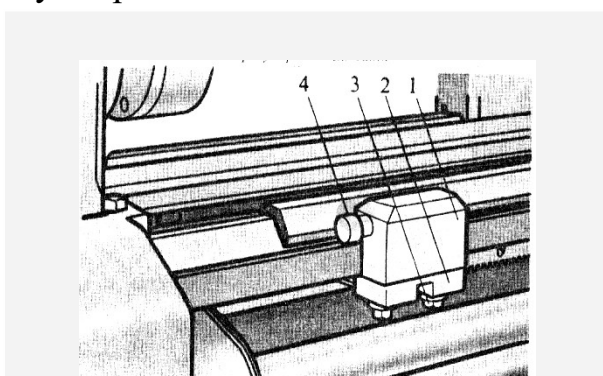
Продольный упор к токарному станку: 1 – корпус упора; 2 – прижимная планка; 3 – зажимной винт; 4 – регулировочный винт
